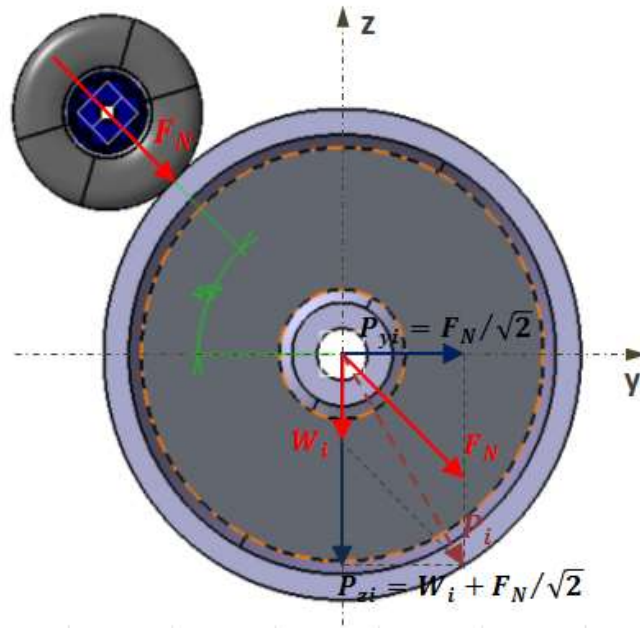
Descomposición de fuerzas en el eje del conjunto de volantes.
